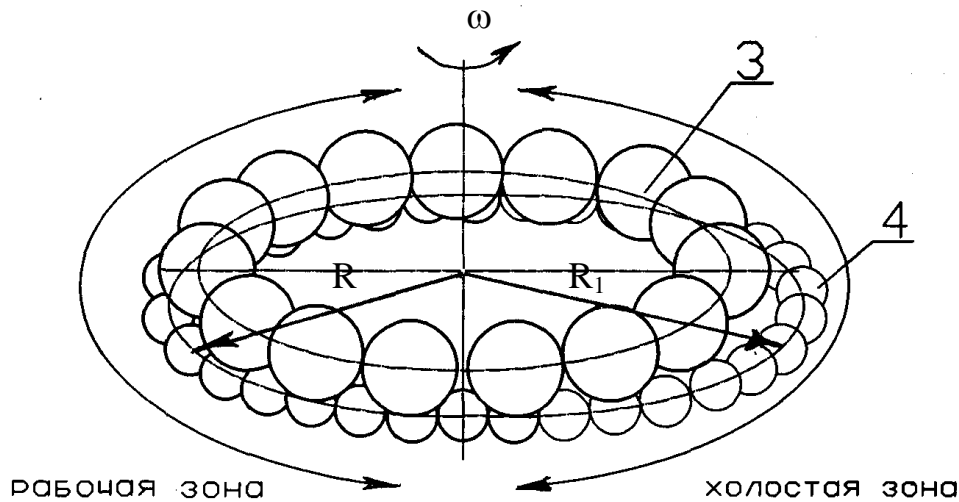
Схема движения приводящих (3) и деформирующих (4) шаров в кольцевой камере инструмента [3]
